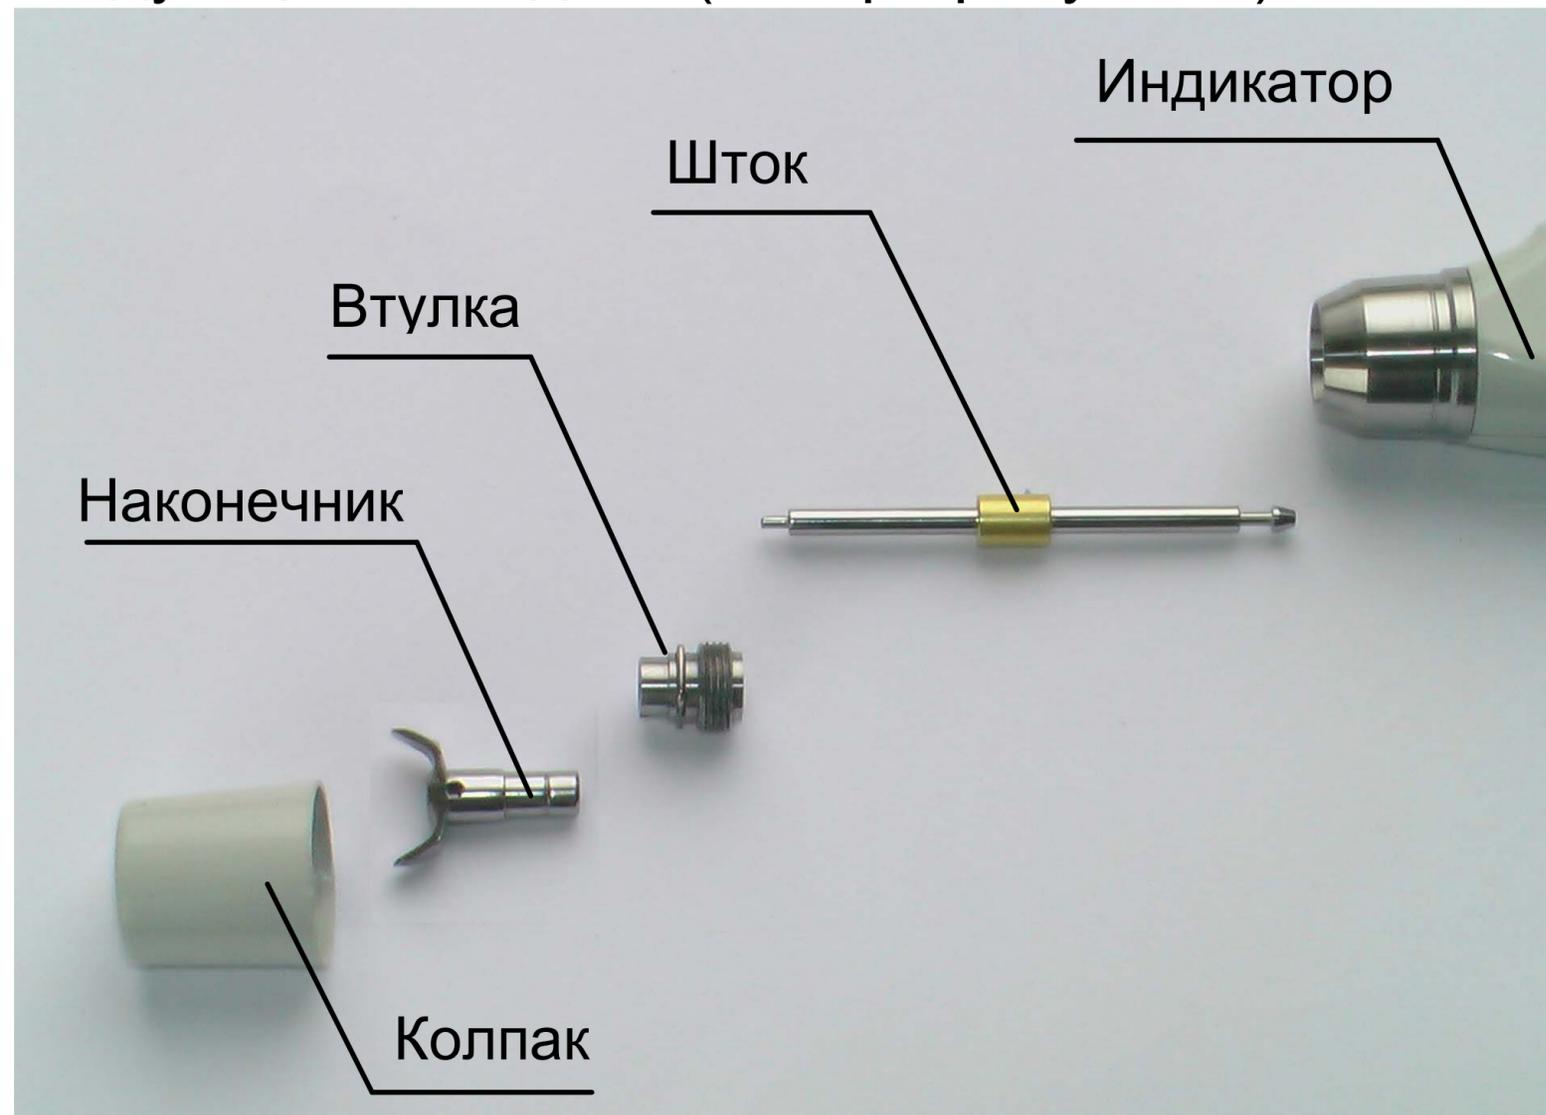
Подготовка индикатора к очистке штокового механизма
